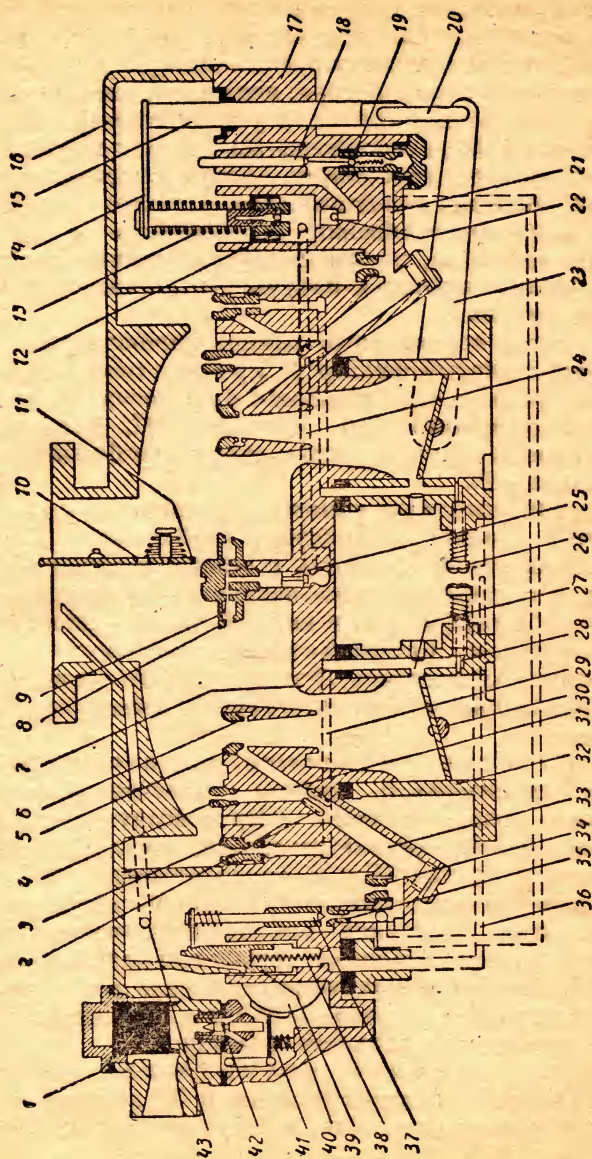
Схема двухкамерного карбюратора К-88 двигателя ЗИЛ-130
